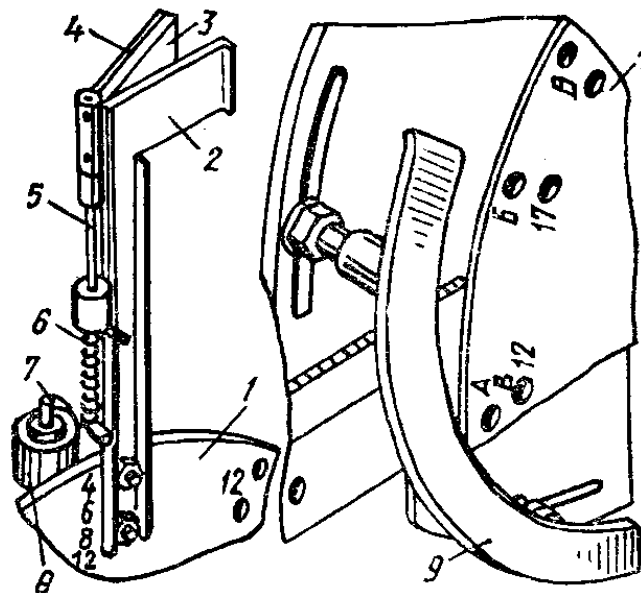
Садильний апарат машини СКН-6А: 1 – диск; 2 – нерухомий стояк з пластиною; 3 – гумова накладка; 4 – рухома пластина; 5 – вісь; 6 – пружина; 7 – коліно осі; 8 – ролик; 9 – лекало
